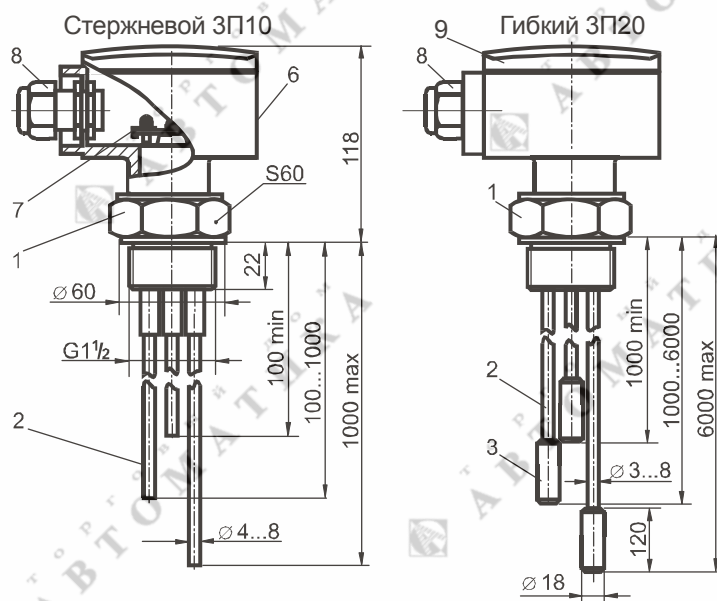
Датчики трехэлектродные, внешний вид и габаритные размеры
